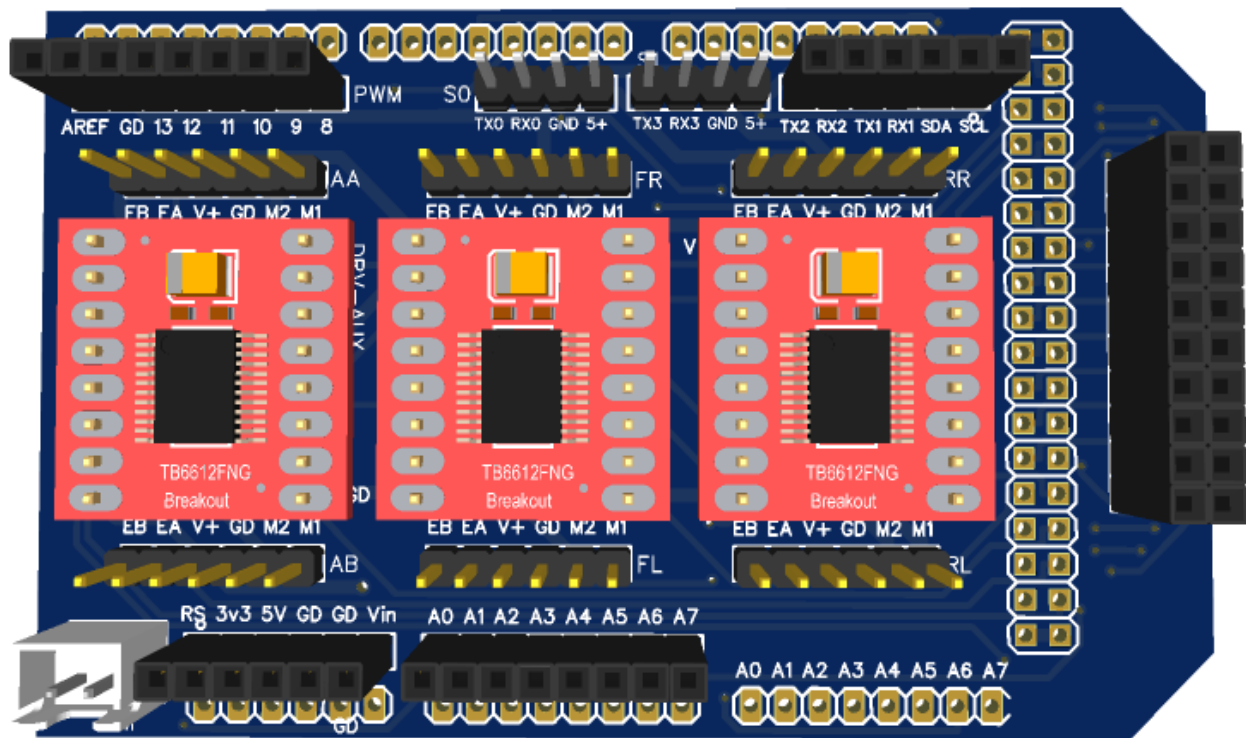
PCB Shield para el Arduino Mega 2560, vista superior.
